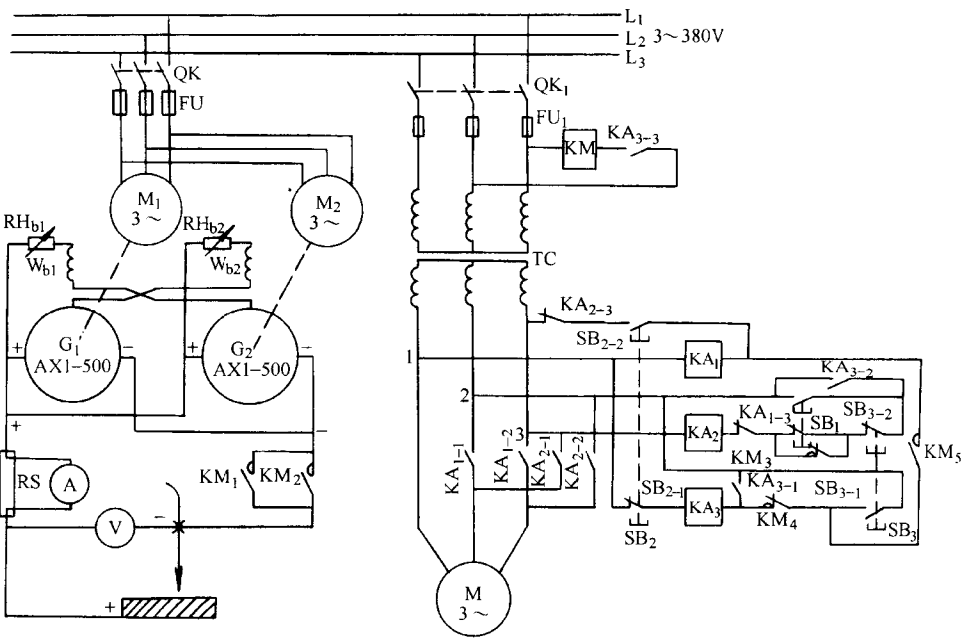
用两台 AX1-500 弧焊发电机并联作为电源用于 MZ1-1000 的直流埋弧焊机接线原理图
